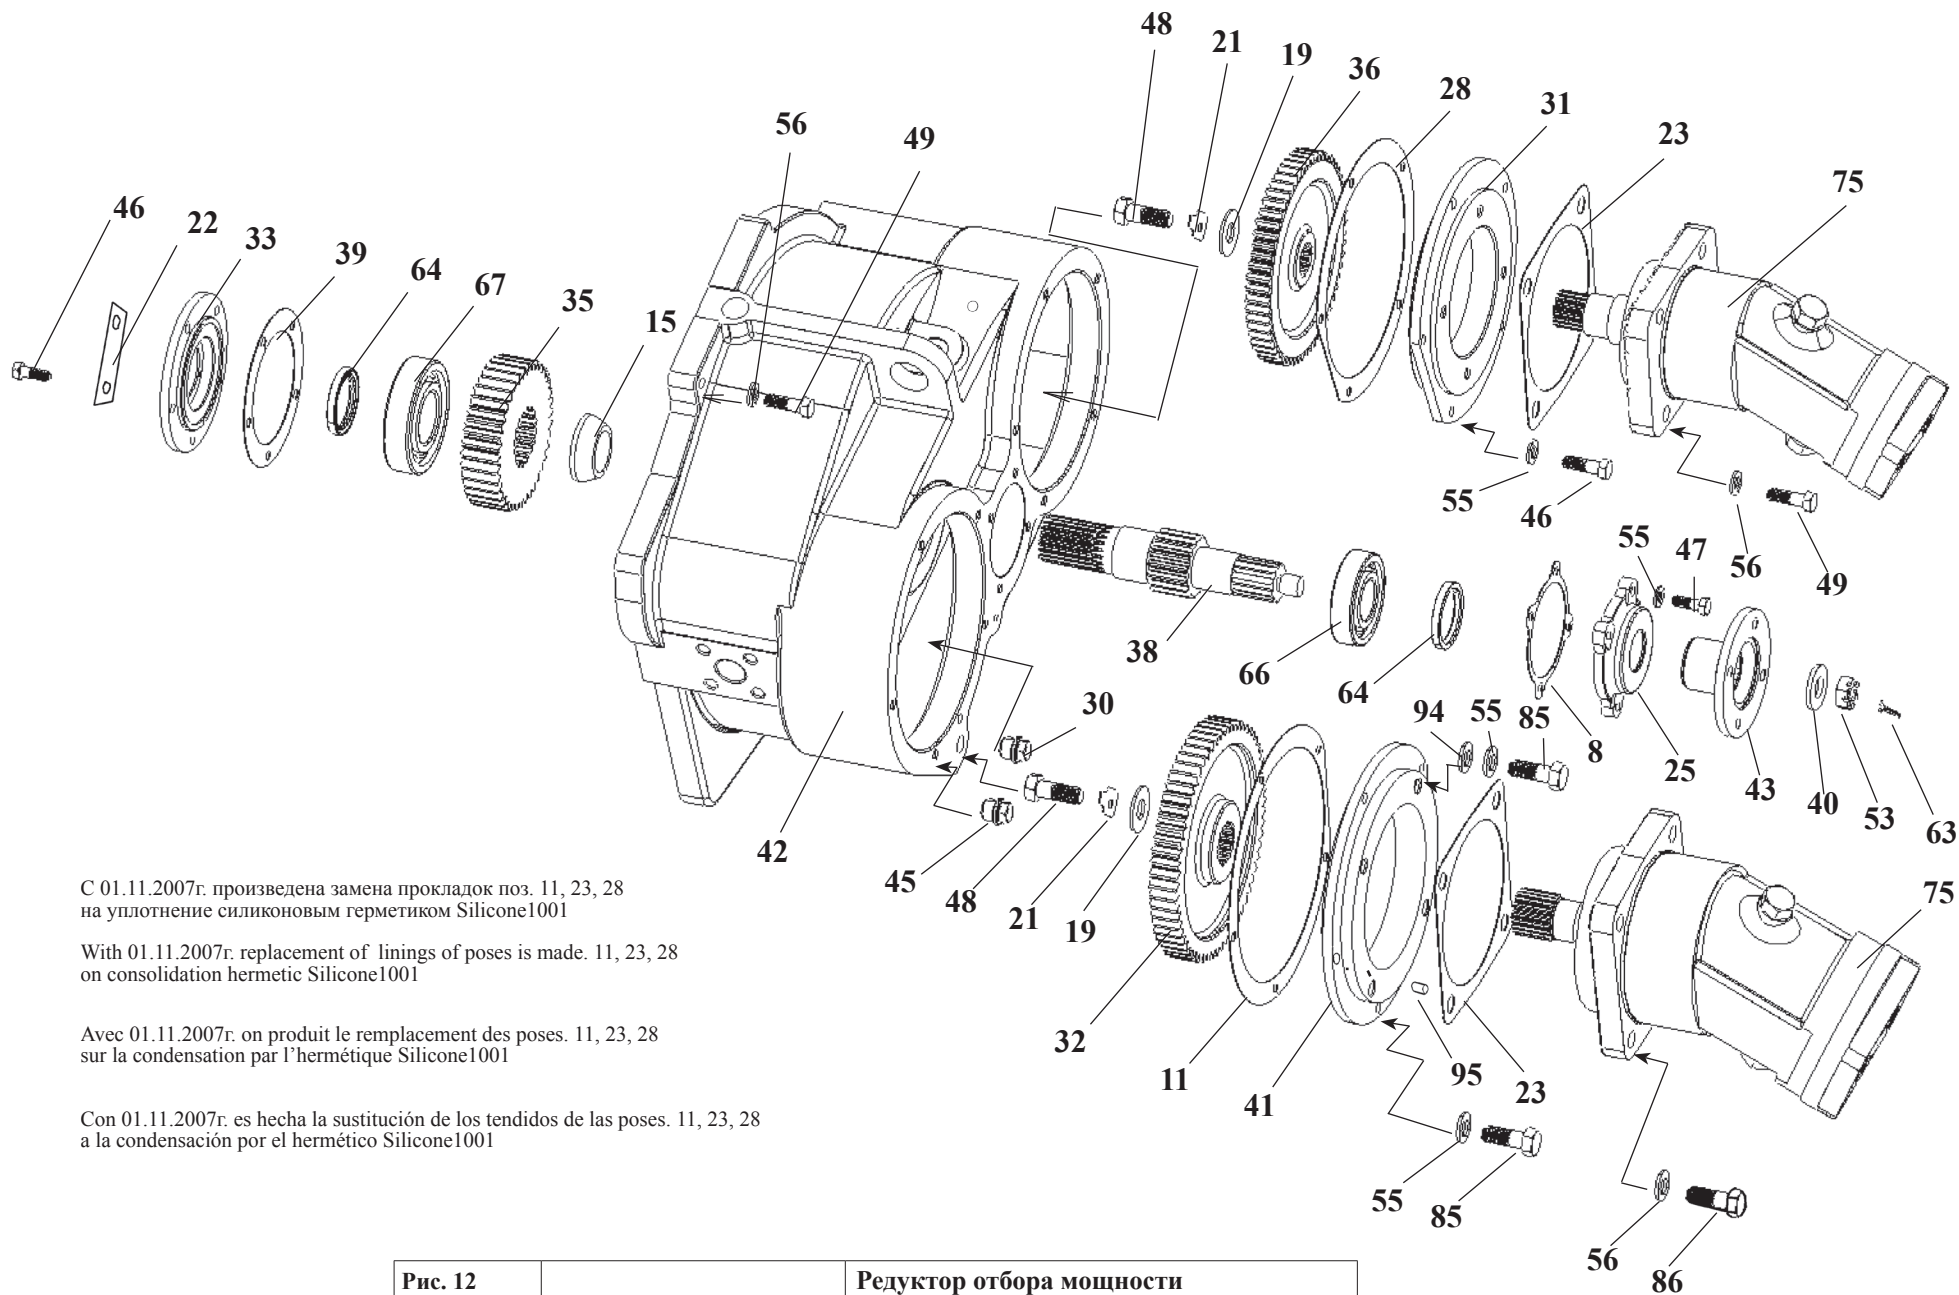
TO-28A.02.04.000-03	Редуктор отбора мощности
